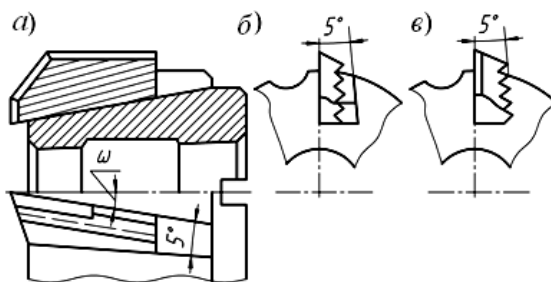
Крепление ножей сборных зенкеров рифлениями
